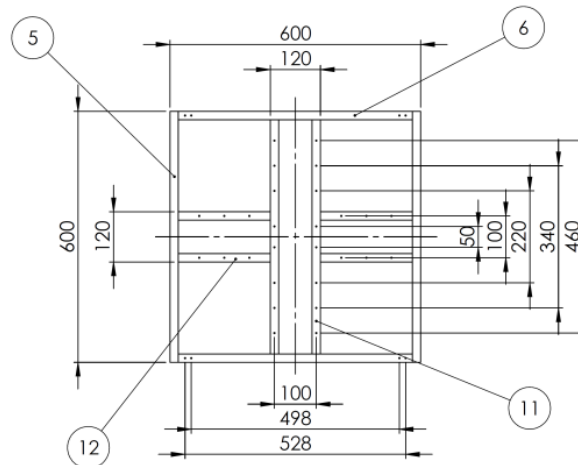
3: Vista superior del ensamble de la estructura. Fuente: Elaboración propia.
